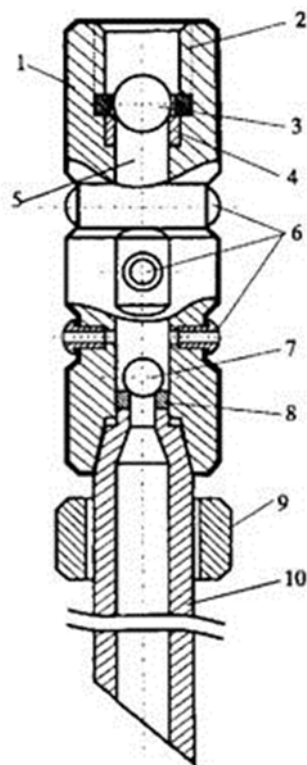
Принципиальная схема аппарата для гидropескоструйной перфорации АП-6м: 1 — корпус перфоратора; 2 — резьба для соединения; 3 — шар опрессовочного клапана; 4 — седло опрессовочного (верхнего) клапана; 5 — канал; 6 — насадка; 7 — нижний шар малого диаметра; 8 — седло нижнего парового клапана; 9 — центратор; 10 — хвостовик.
